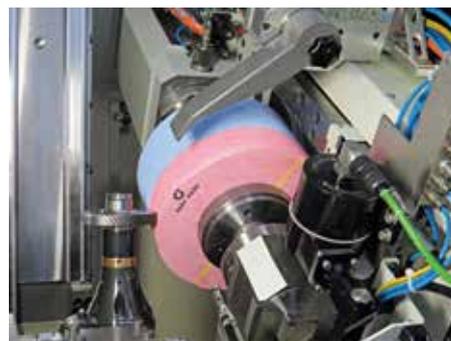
Kombiniertes Werkzeug mit konventionellem und Feinschleif-Anteil.
